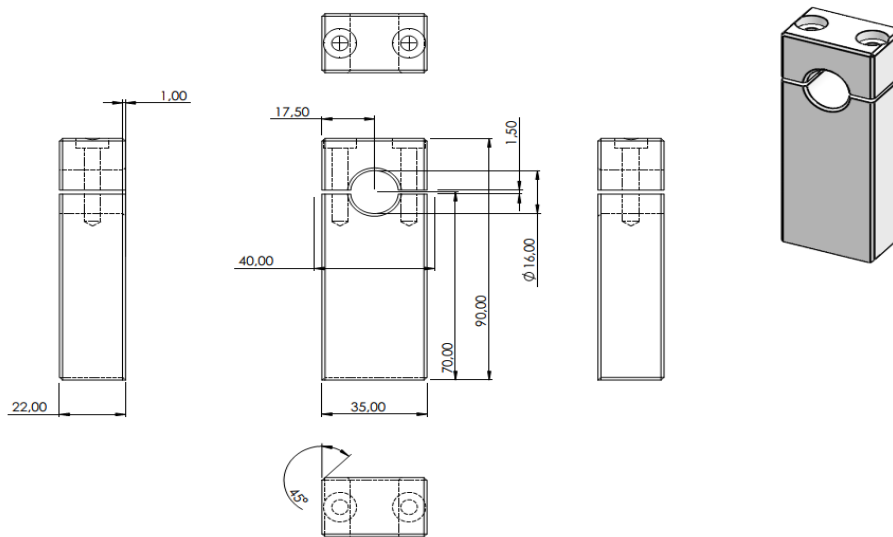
Mise en plan du support de fixation sur SolidWorks.
